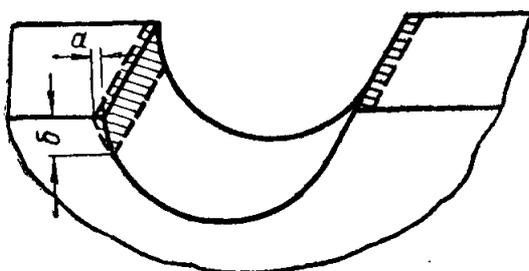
«Развалка» посадочных поверхностей разъемных корпусов
